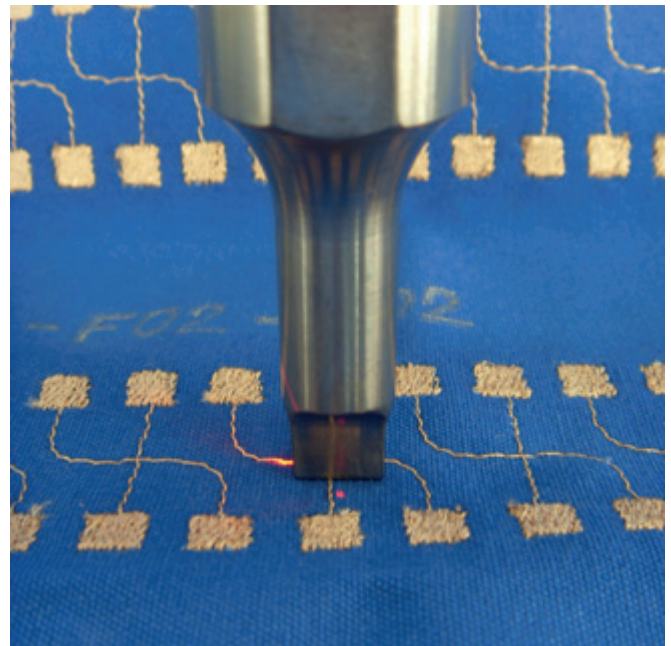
Ultraschall-Schweißung zur Erzeugung eines elektrischen Kontaktes sich kreuzender gestickter Leiter
